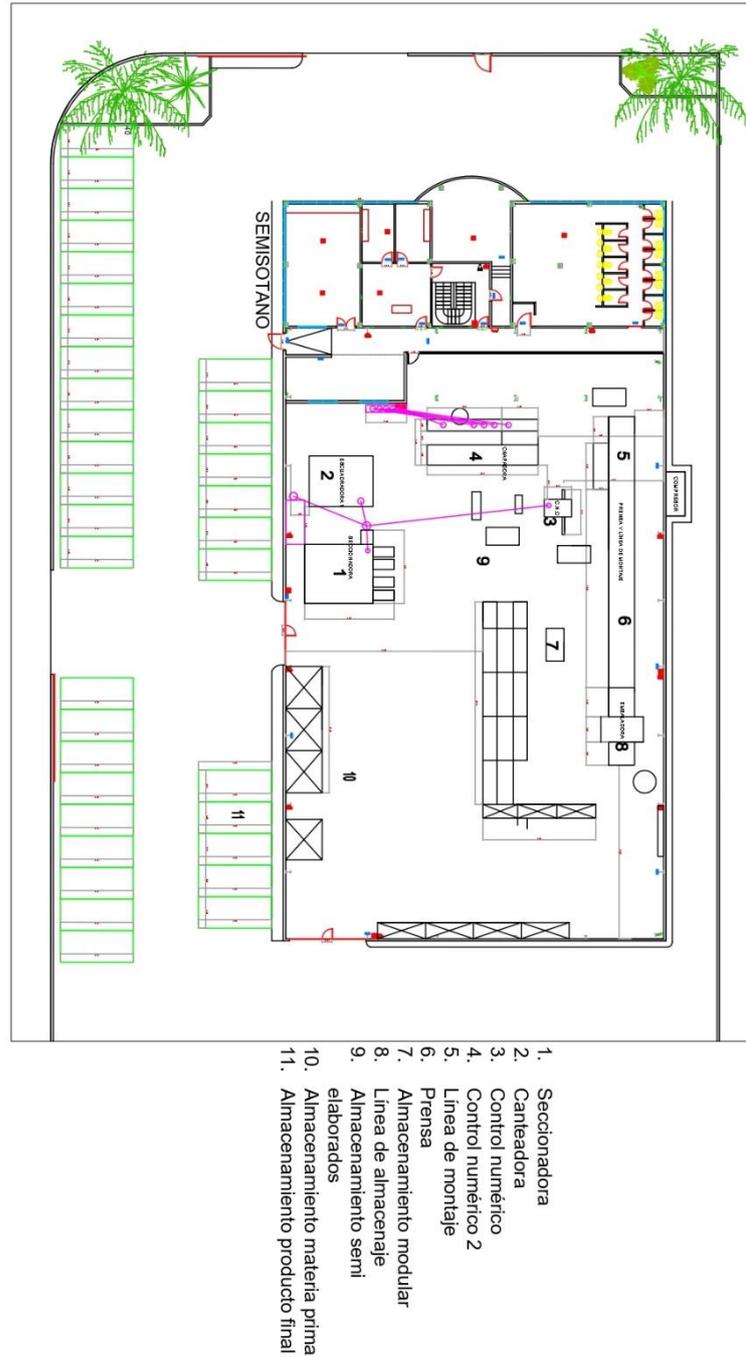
Plano de planta. Fuente: Avant Area (2025)
